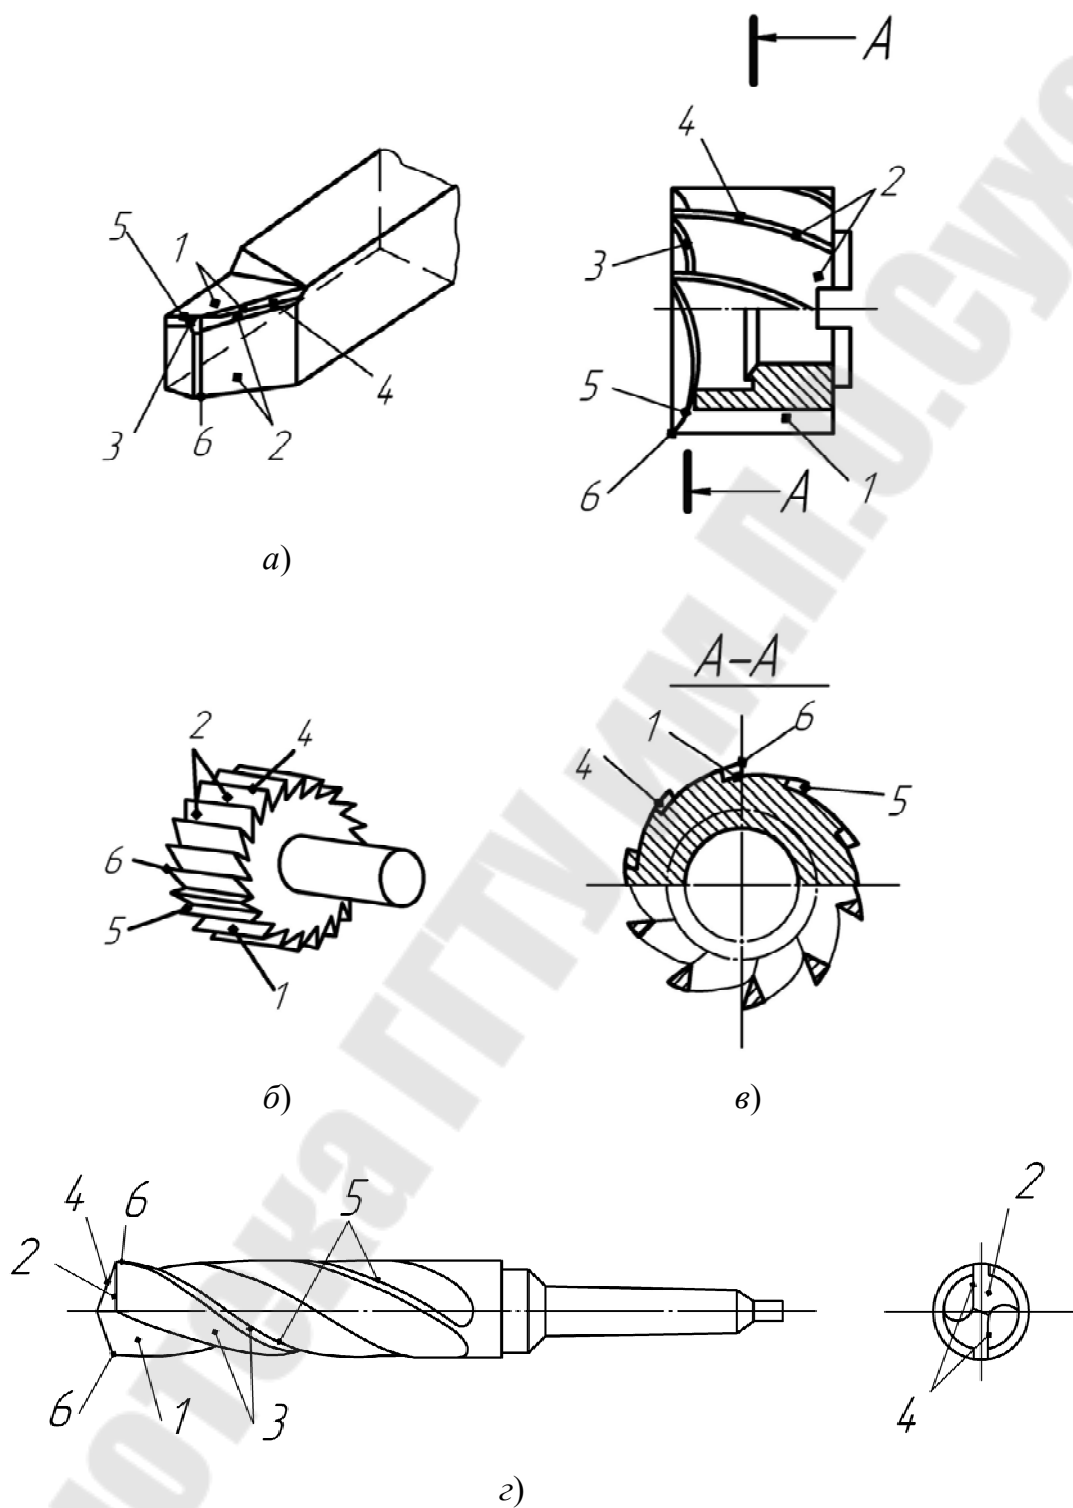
Элементы токарного проходного резца (а), угловой концевой фрезы (б), периферийно-торцевой фрезы (в) и винтового сверла (г):
